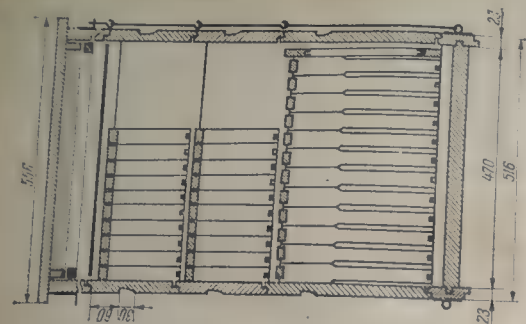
Secțiune longitudinală și transversală în stupul vertical cu magazine
